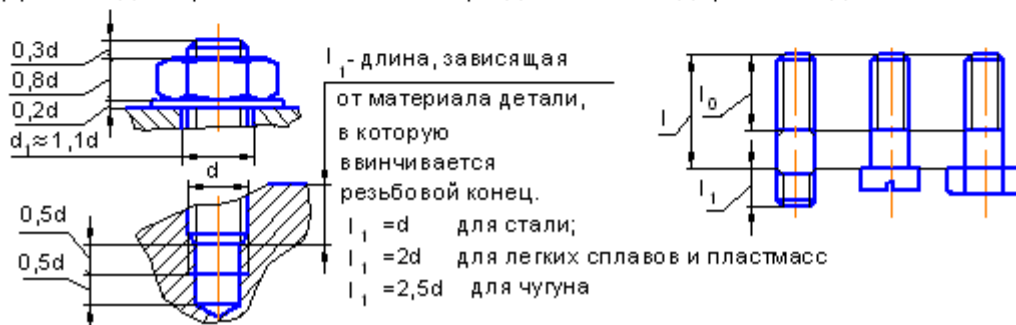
Данные по выбору длины винта, болта, шпильки
